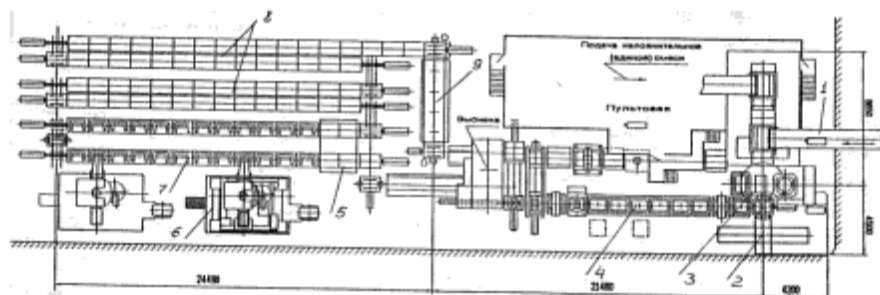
Автоматическая формовочная импульсной формовки с нижним прессованием НИИТАвтомпрома (Литаформ): 1 – транспортер подачи облицовочной формовочной смеси; 2 – механизм смены модельной оснастки; 3 – четырехпозиционный формовочный автомат; 4 – участок сборки форм; 5 – загрузка форм перед заливкой; 6 – автоматическая установка для заливки форм; 7 – участок заливки форм; 8 – участок охлаждения залитых форм; 9 – передача залитых форм на выбивку.
